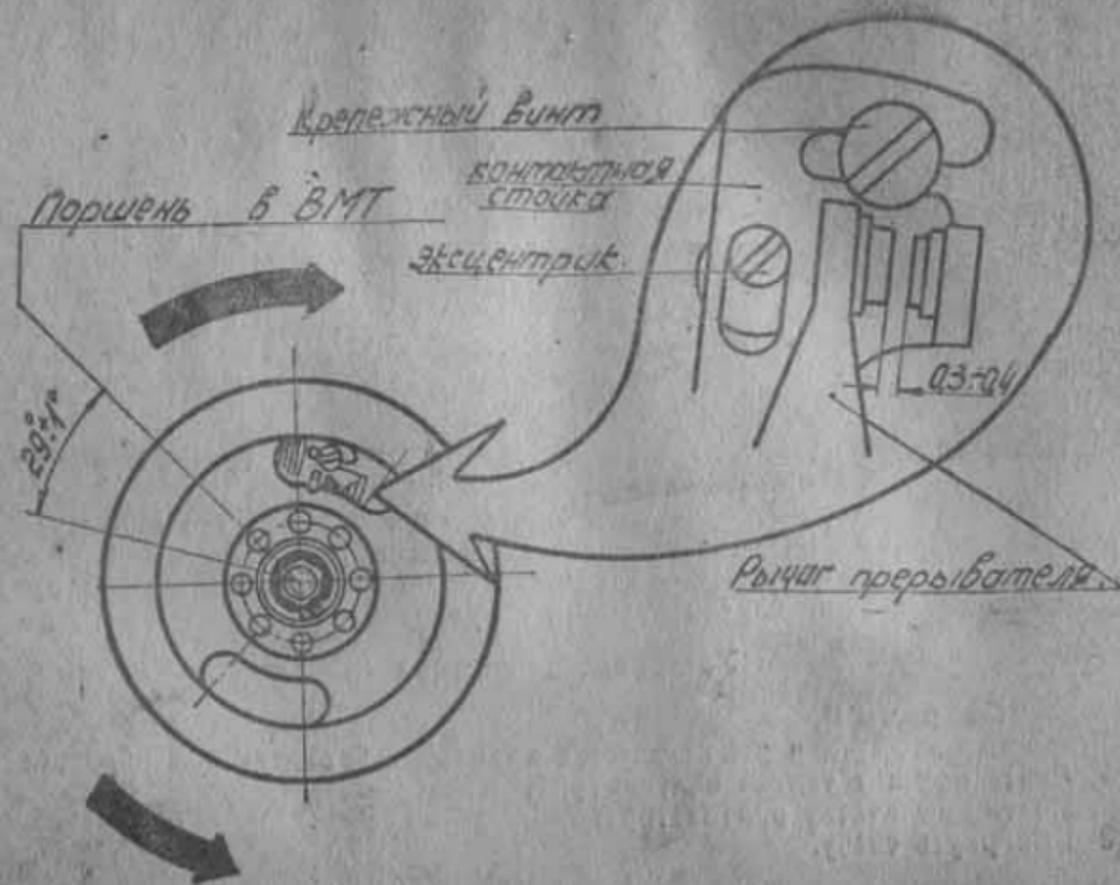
СХЕМА УСТАНОВКИ ЗАЖИГАНИЯ
